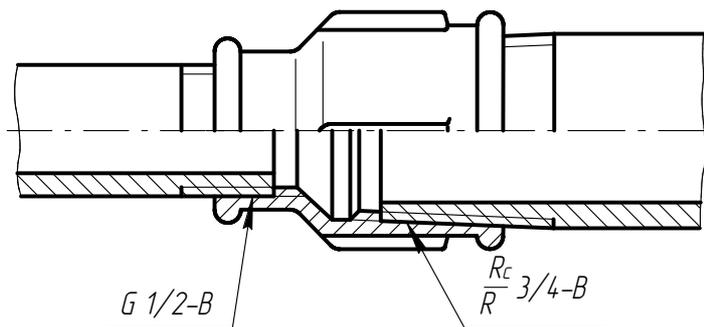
Пример простановки обозначения трубных резьб на сборочном чертеже
